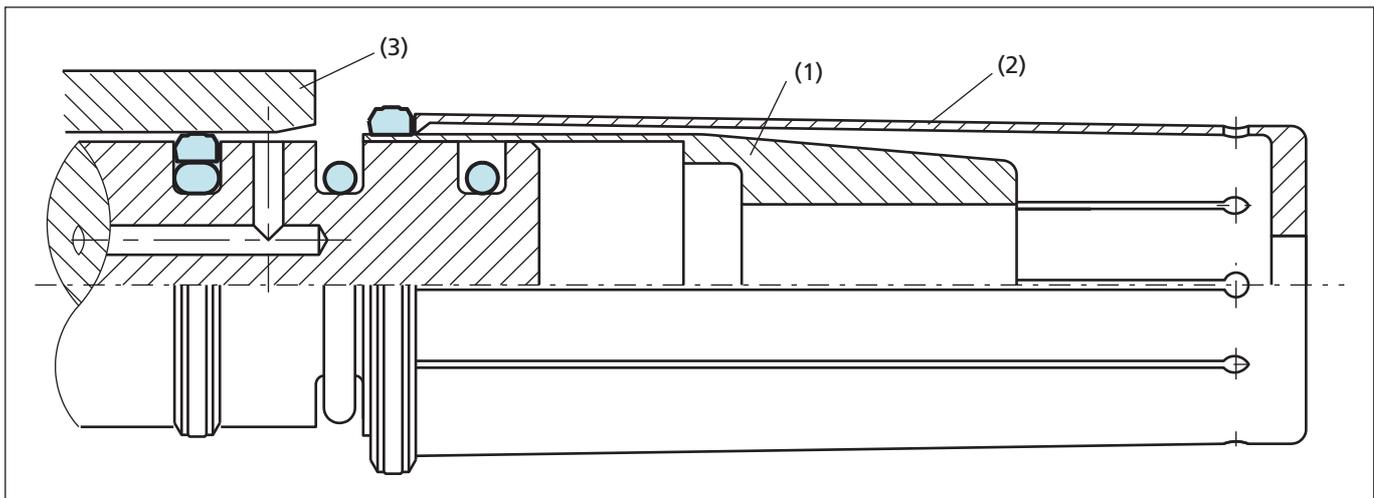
Aufdehnen des Zurcon® Roto Glyd Ring® S über die Montagehülse mittels einer Sprezhülse
